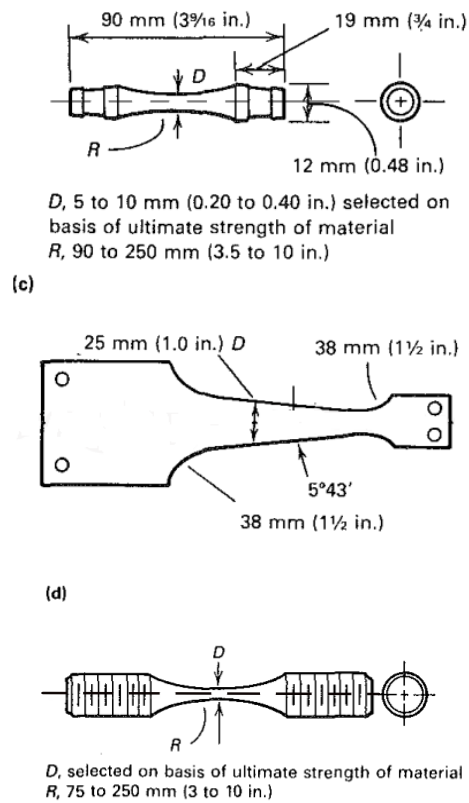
Éprouvettes d'essai de fatigue -2-[12]
